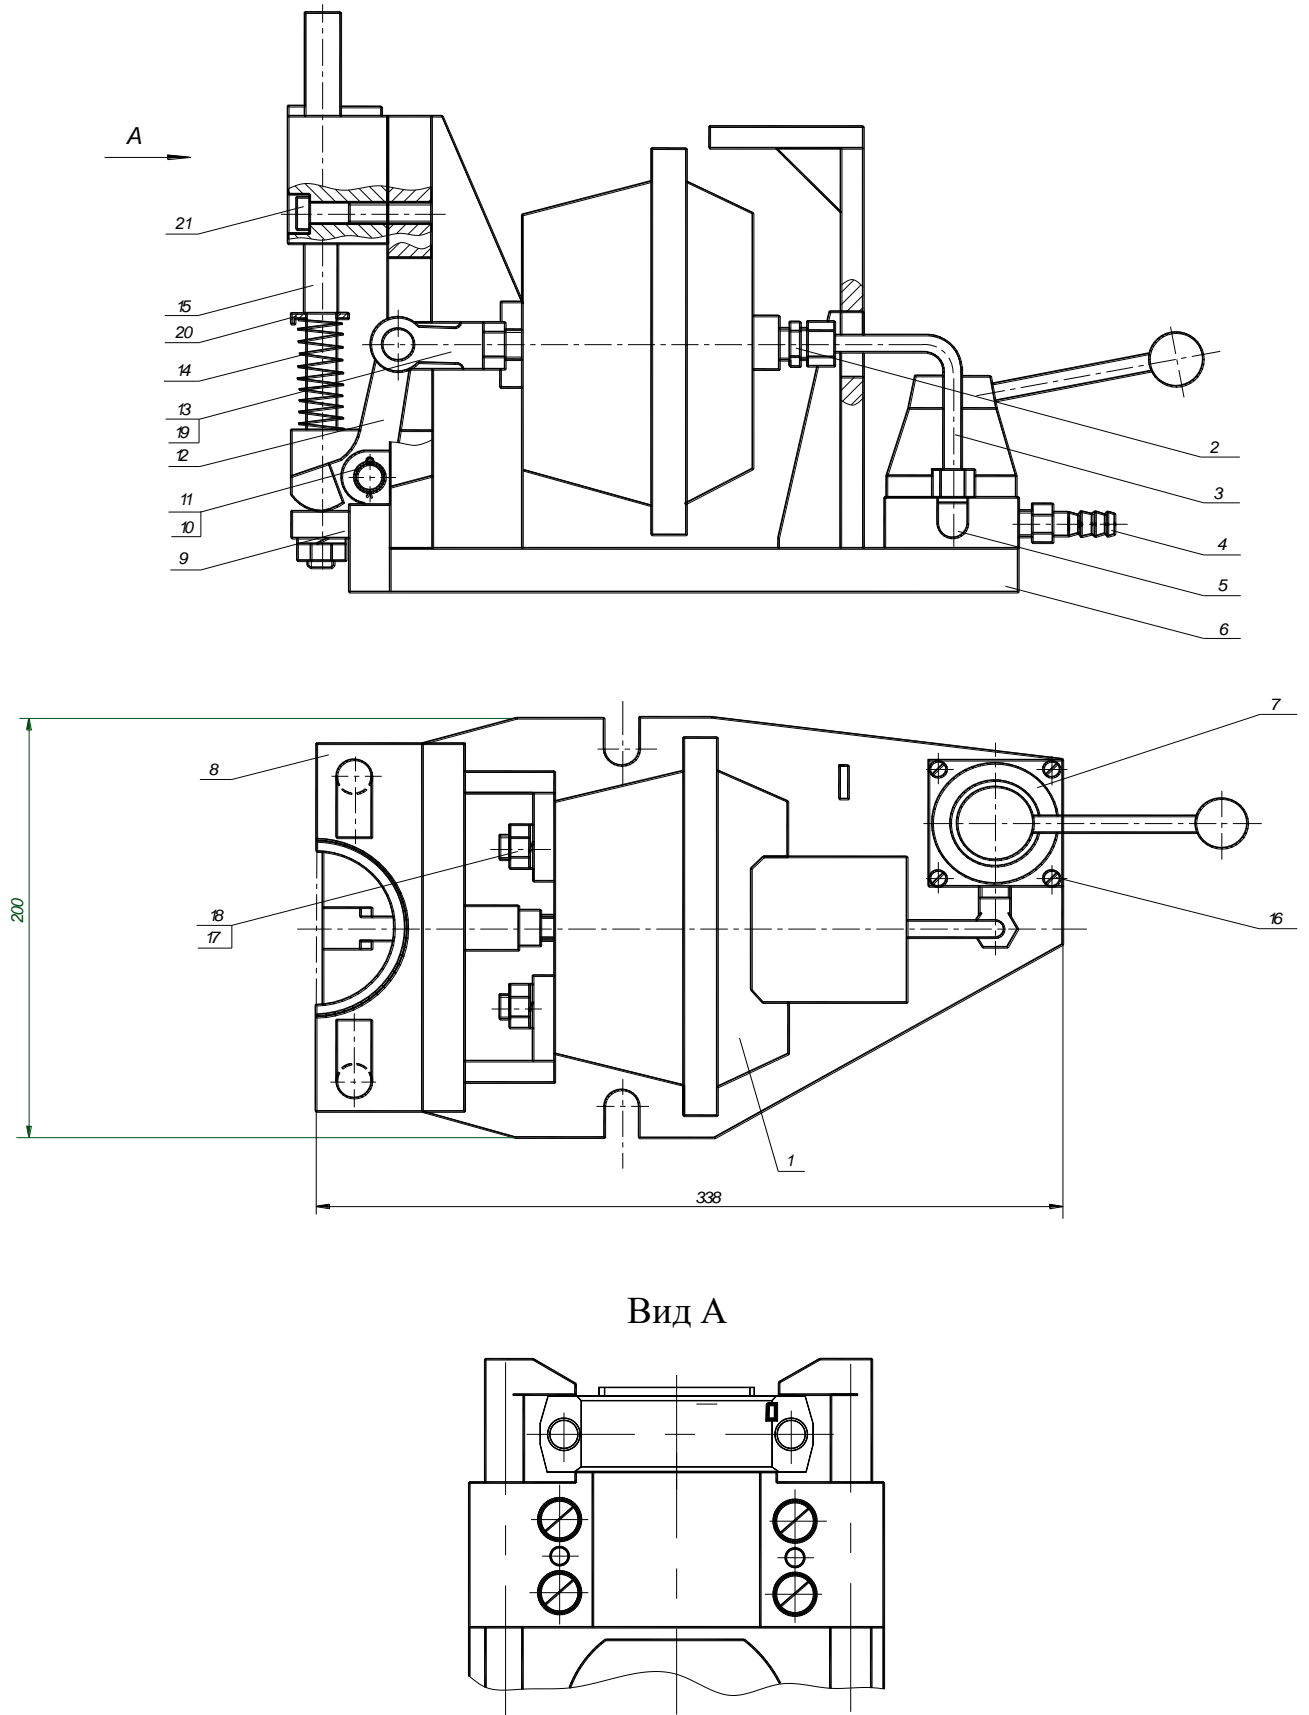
Пристосування для закріплення деталі при фрезеруванні пазів в шатуне і кришці шатуна під вкладиші
